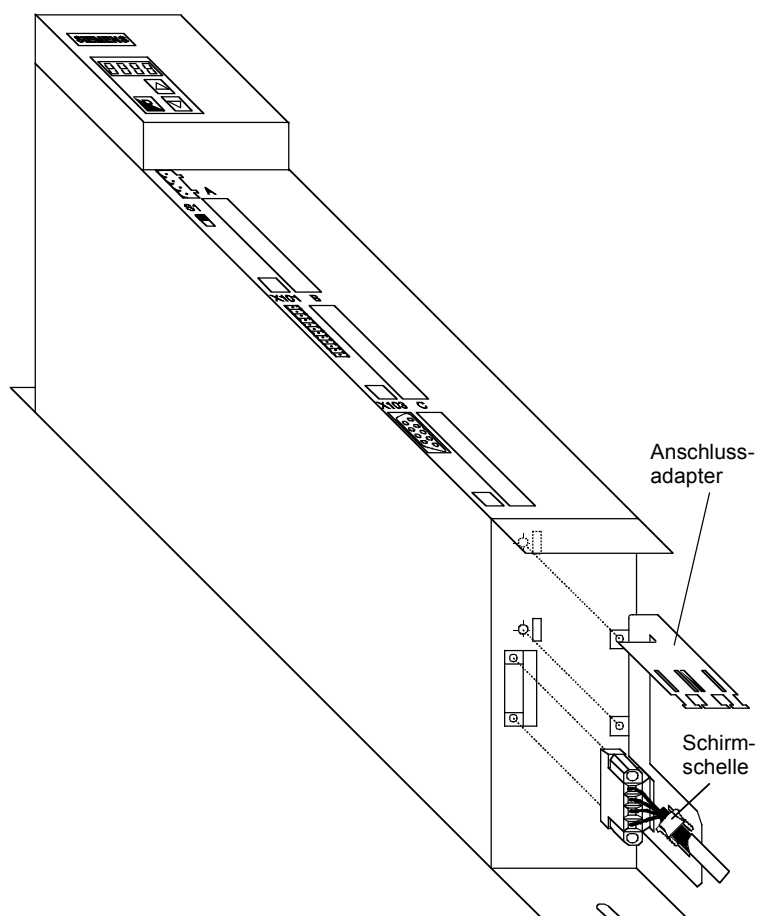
Montage des Motoranschlusses und des Anschlussadapters
